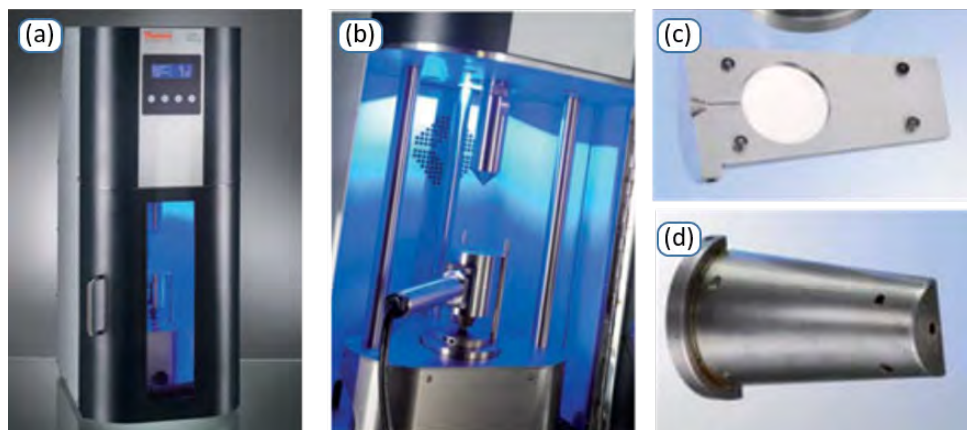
(a) et (b) Photographies de la machine à injection HAAKE Minijet II avec (c) et (d) le moule utilisé pour réaliser les pastilles.
